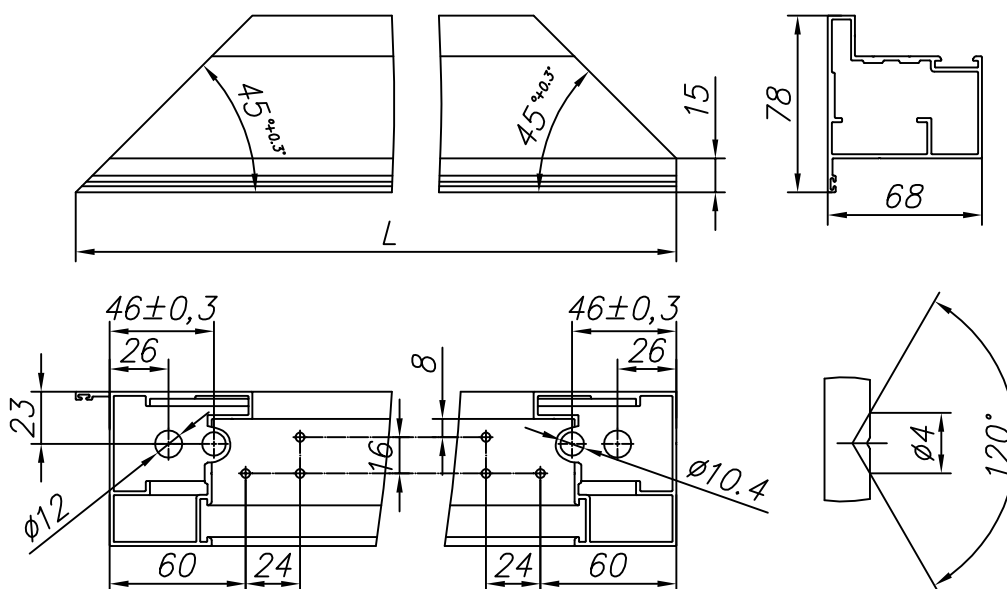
Изготовление стойки без паза для замка из профиля FLGU.400.0108
